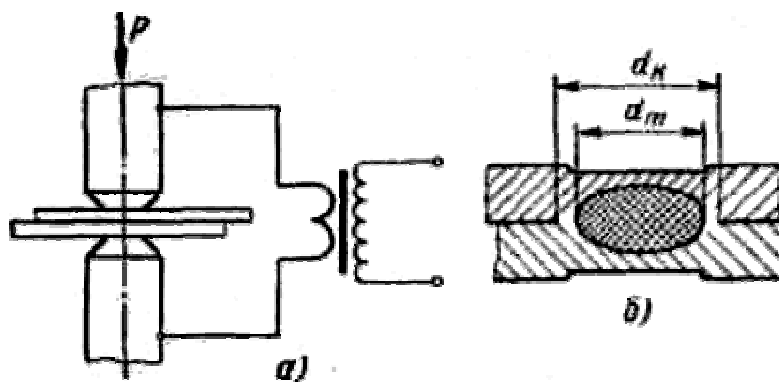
Схема процесса точечной сварки: а — схема процесса; б — сечение сварной точки; P — давление; d_m — диаметр литого ядра сварной точки; d_k — диаметр сварной точки
